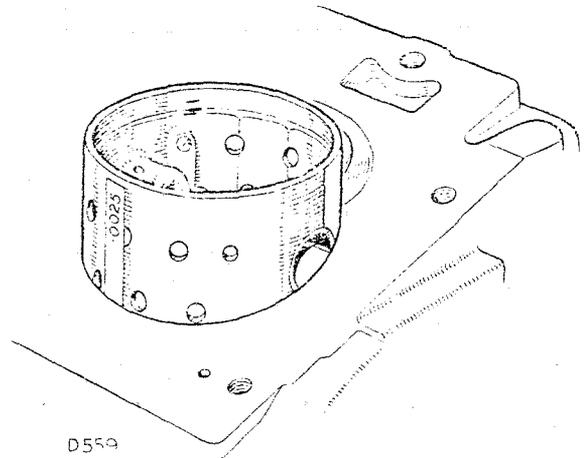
Para verificar la tolerancia del pistón
